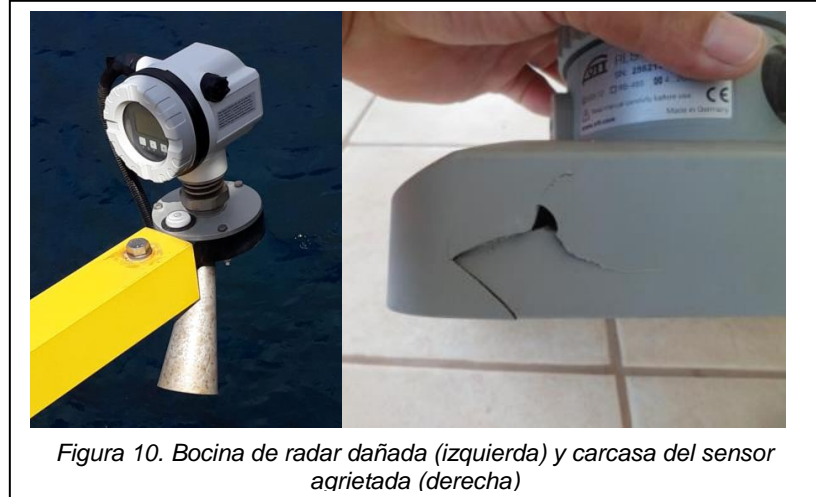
Bocina de radar dañada (izquierda) y carcasa del sensor agrietada (derecha)
